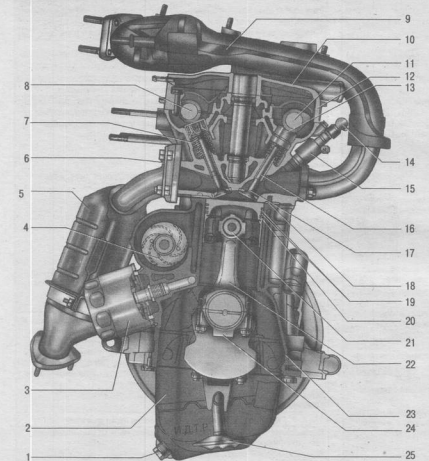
Поперечный разрез двигателя ВАЗ-11194: 1 – пробка сливного отверстия; 2 – масляный картер; 3 – масляный фильтр; 4 – водяной насос; 5 – катколлектор; 6 – выпускной клапан; 7 – пружина клапана; 8 – распределительный вал выпускных клапанов; 9 – впускной коллектор; 10 – крышка головки блока цилиндров; 11 – распределительный вал впускных клапанов; 12 – гидравлической толкатель клапана; 13 – корпус подшипников распределительных валов; 14 – топливная рампла; 15 – форсунка; 16 – направляющие втулка клапана; 17 – впускной клапан; 18 – прокладка головки блока цилиндров; 19 – компрессионные кольца; 20 – масляное кольцо; 21 – поршневой палец; 22 – шатун; 23 – блок цилиндров; 24 – крышка шатуна; 25 – маслоприемник
